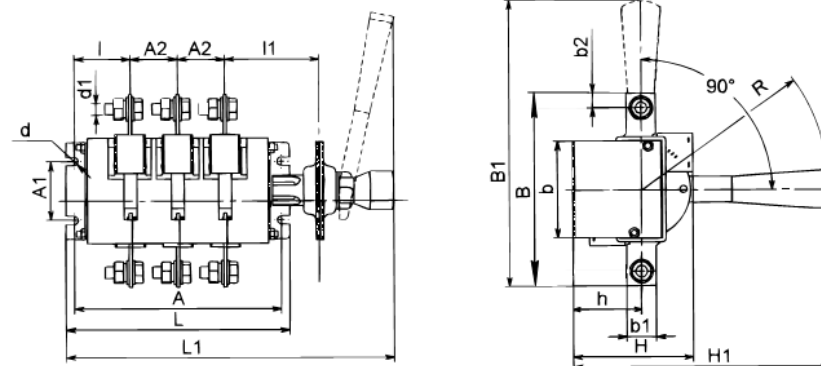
Б Выключатель-разъединитель на одно направление трехполюсный с боковой смещенной рукояткой
